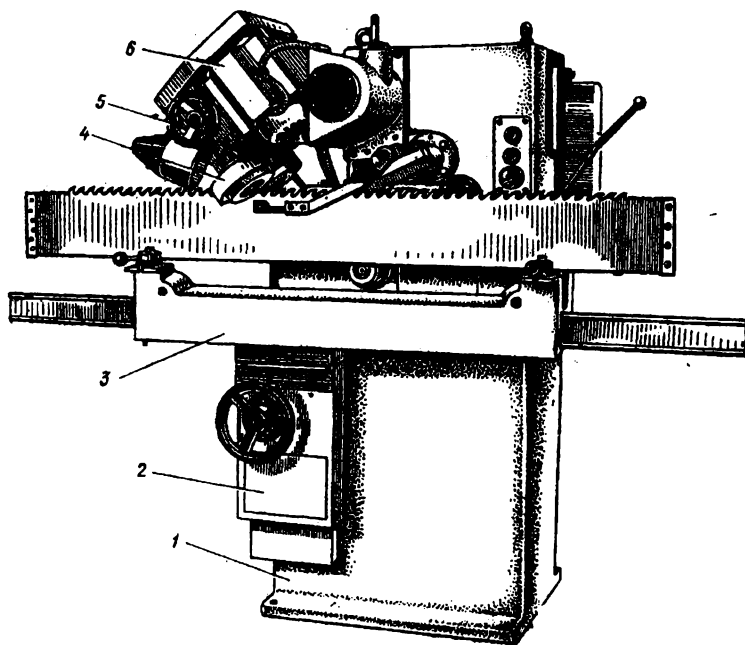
Станок для боковой заточки зубьев рамных пил после наплавки стеллитом
